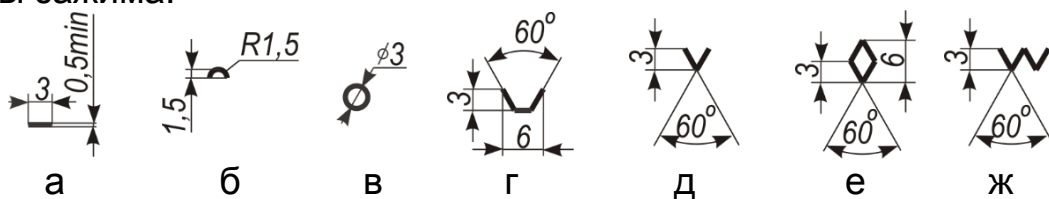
Обозначение формы рабочей поверхности:
